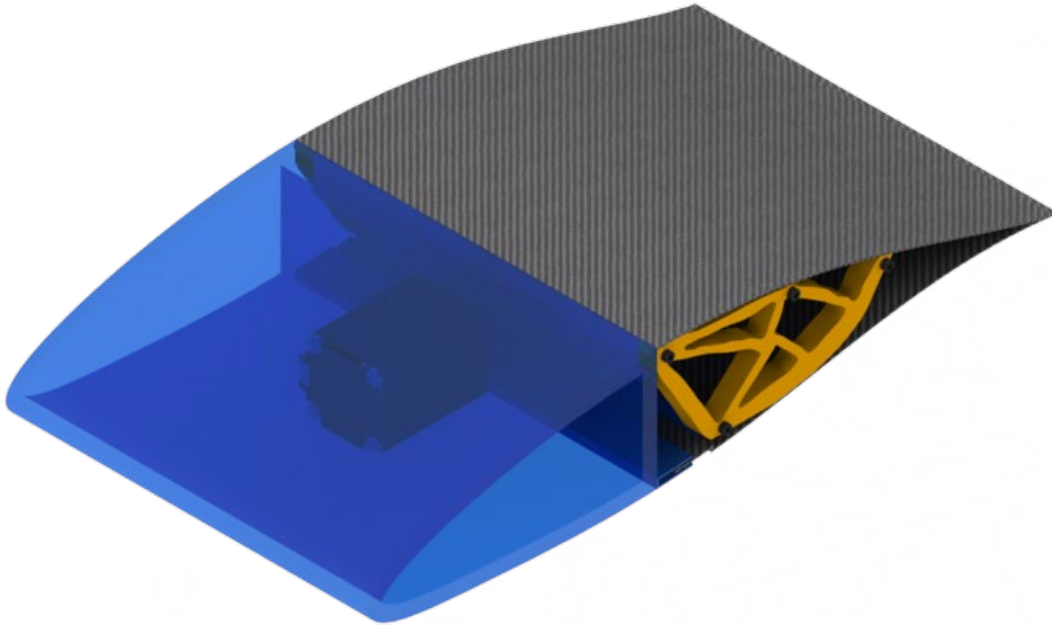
Diseño detallado, vista frontal. Fuente: Autor.
